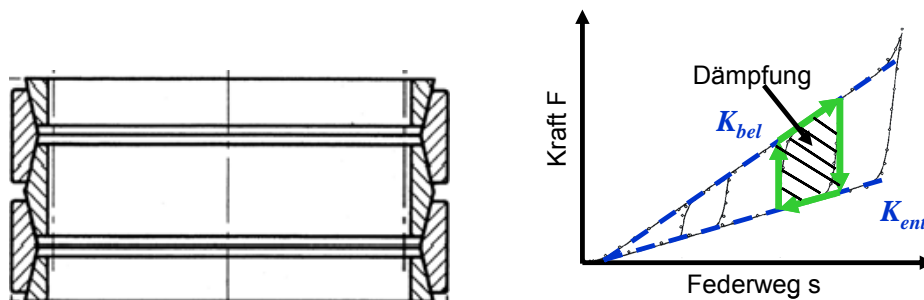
links: Ringfederpaket; rechts: Kraft-Weg-Diagramm einer Ringfeder
